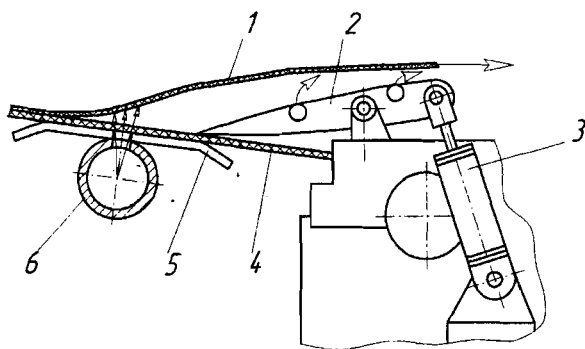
Воздушный шабер для заправки бумаги: 1 – бумажное полотно; 2 – шабер с отверстиями для сжатого воздуха; 3 – привод шабера; 4 – прессовое сукно; 5 – направляющая пластина; 6 – воздушное сопло
